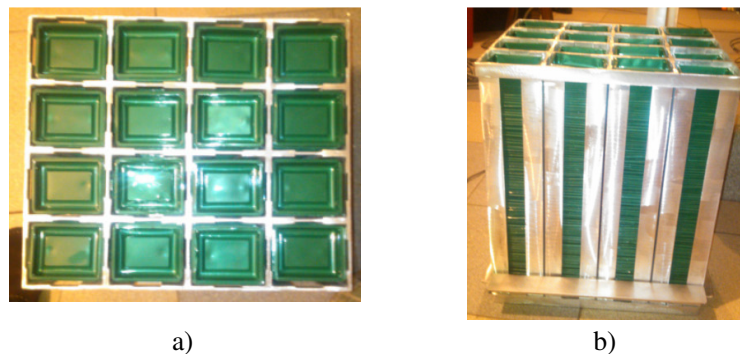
Versão final do armazém com as pilhas de escorredores: a) Vista de topo; b) Vista lateral
